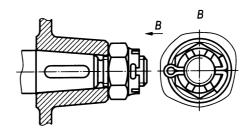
Крепление корончатой гайкой и шплинтом
